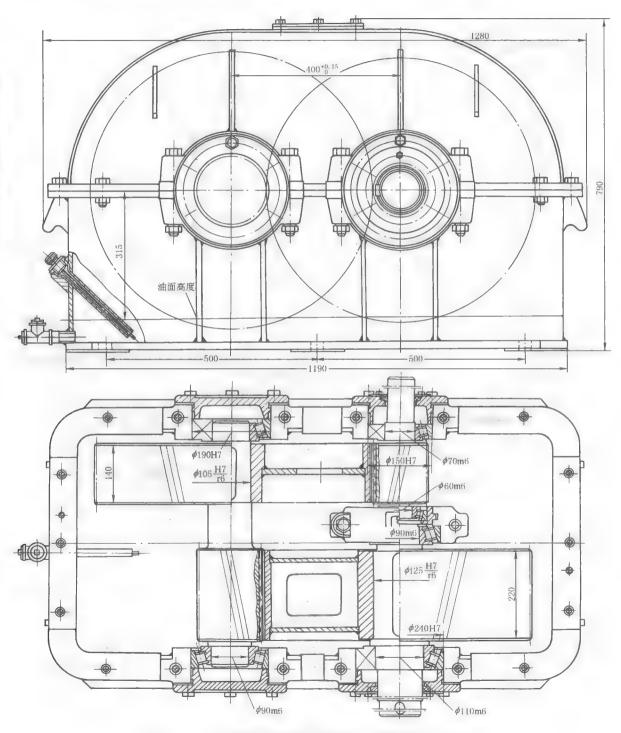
两级同轴式圆柱齿轮减速器 (焊接箱体和大齿轮)
